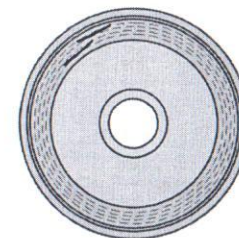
Контроль наружной поверхности обода колеса
